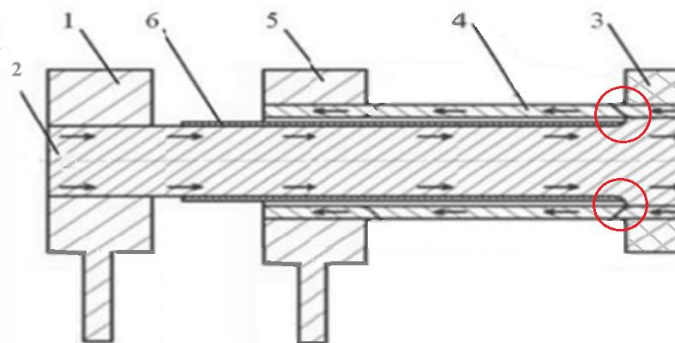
Система струмопровід – заготованка при прямому пропусканні струму по заготованці
